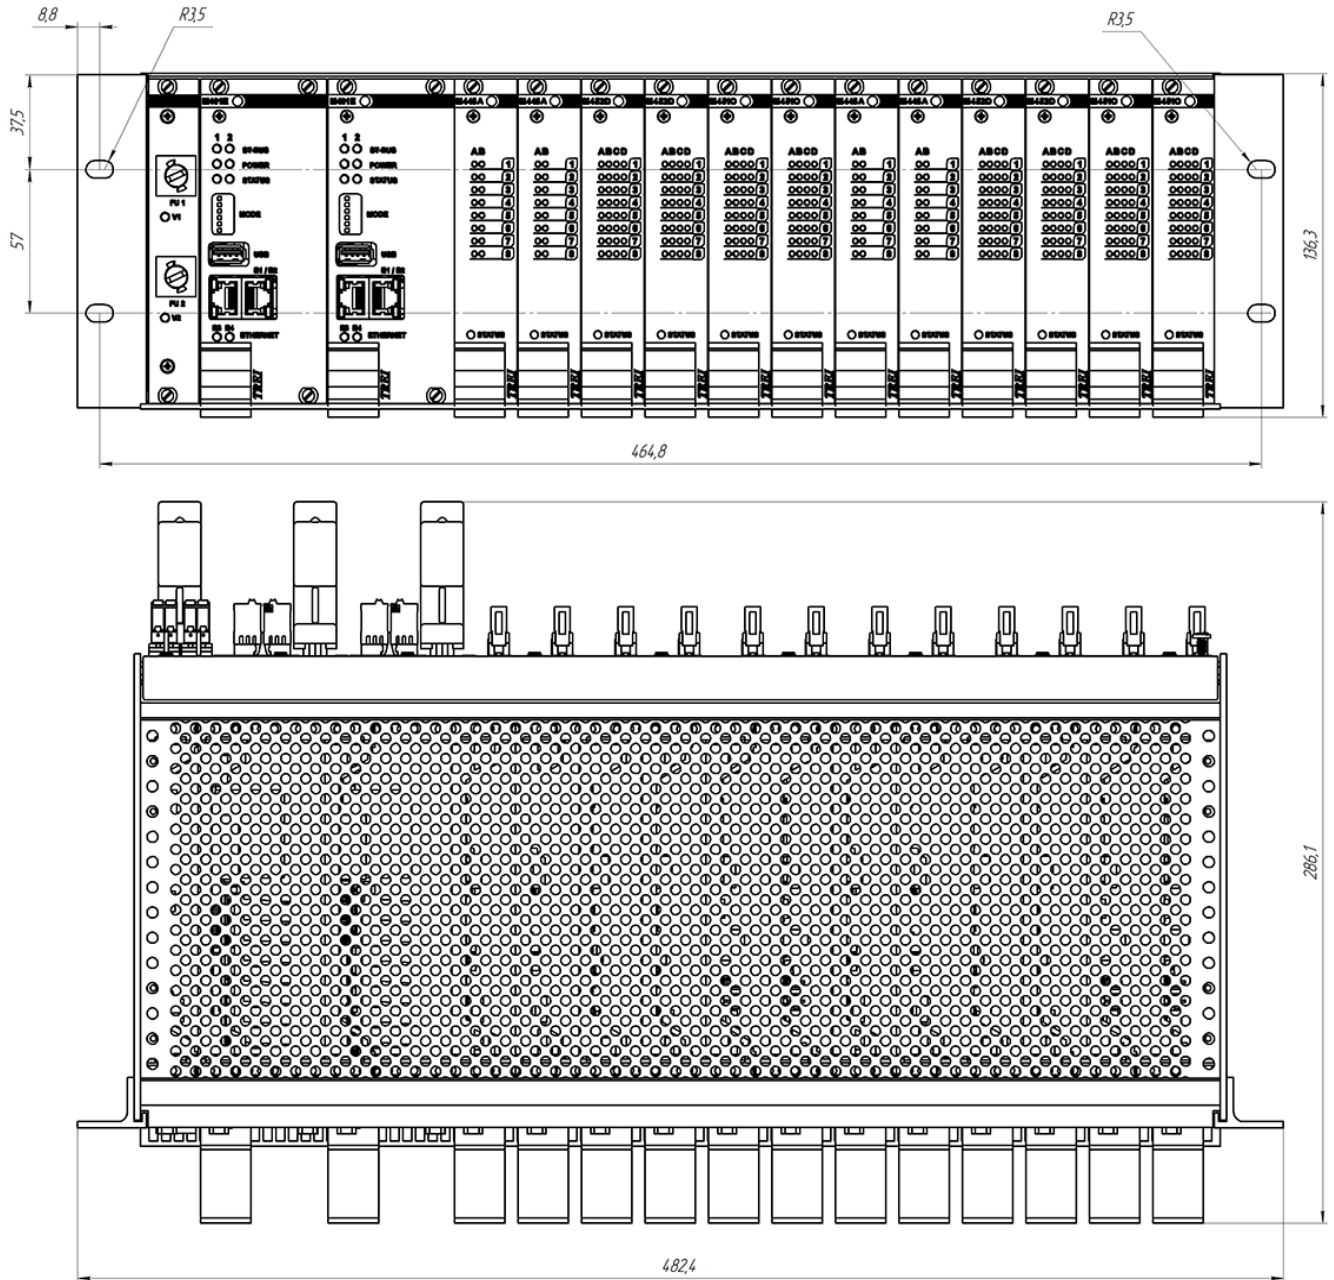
Чертеж общего вида каркаса CR MR с указанием габаритных размеров
